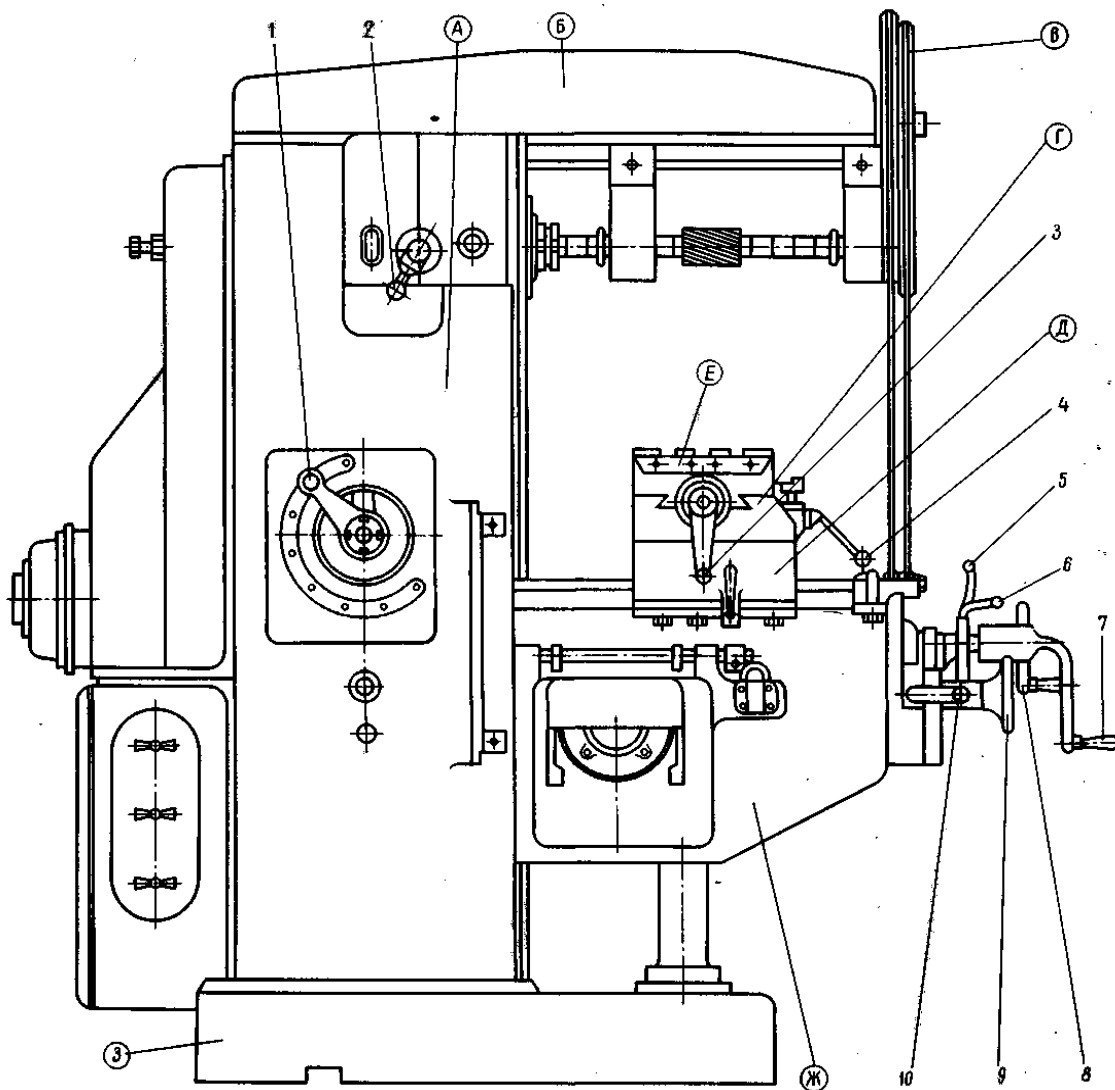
Общий вид универсально-фрезерного станка модели 6Н81
